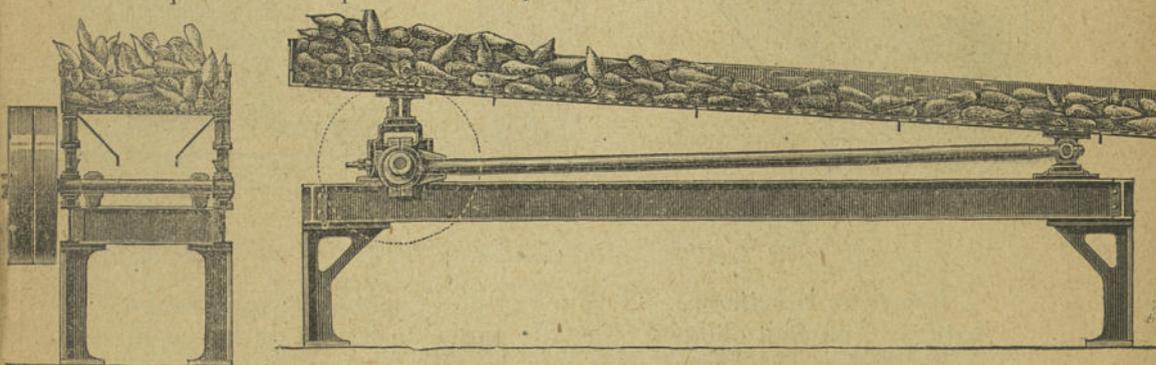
Secoueur de betteraves (Halle'sche Maschinenfabrik).
